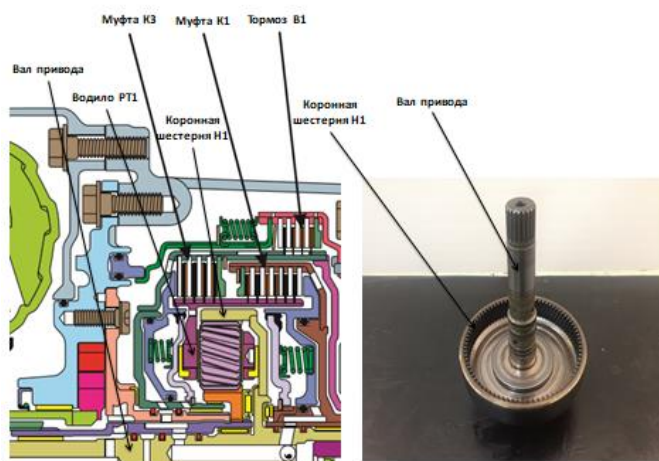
Устройство вала привода и коронной шестерни Н1 в сборе
